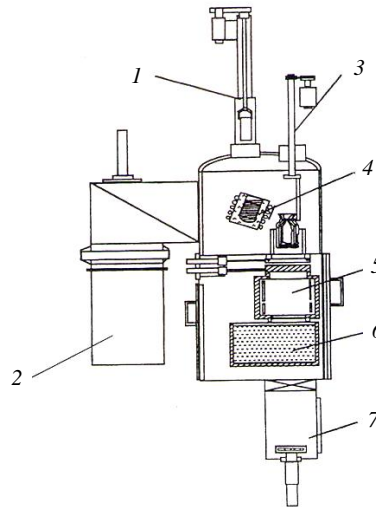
Схема установки VSP 5 DS/SC/LMC (жидкометаллический охладитель – расплав олова): 1 – механизм для загрузки шихты; 2 – вакуумный насос; 3 – система перемещения отливки; 4 – индукционный тигель для плавки; 5 – нагреватель сопротивления для нагрева формы; 6 – емкость с охладителем; 7 – конструкция перемещения формы на кристаллизаторе
